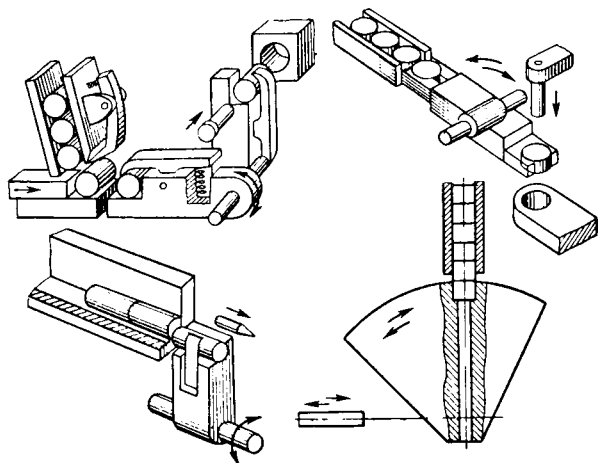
Питатели с колебательным движением держателя с захватом
